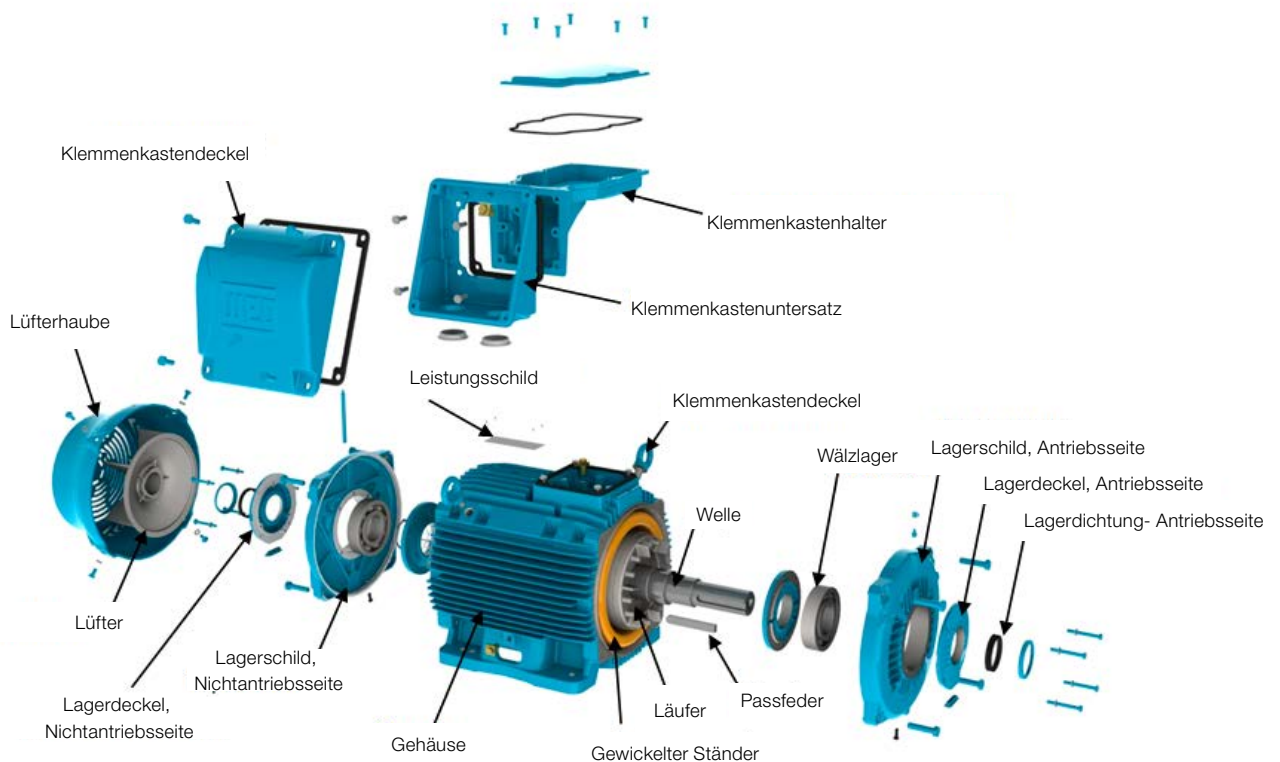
Explosionszeichnung der Bauteile des Motors der Baureihe W22
